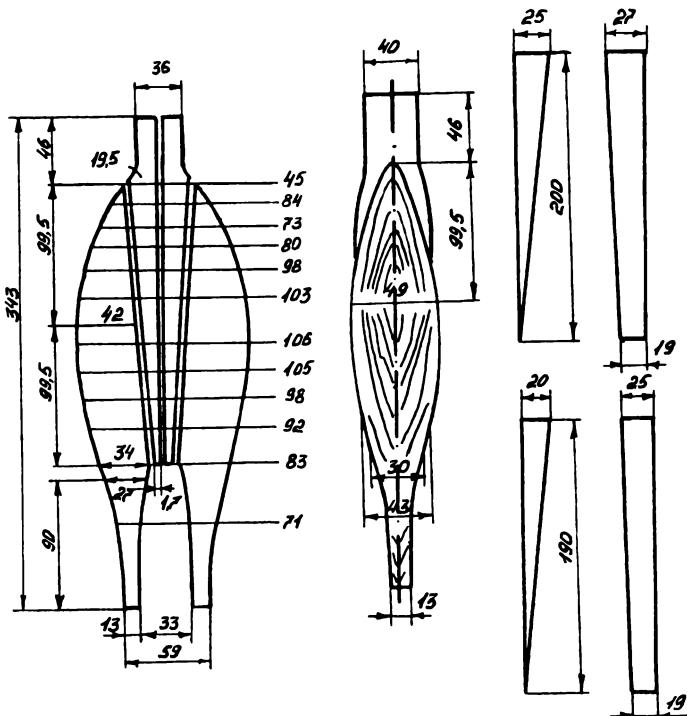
Разборная правилка для шкурок соболя конструкции А.А. Елкова
